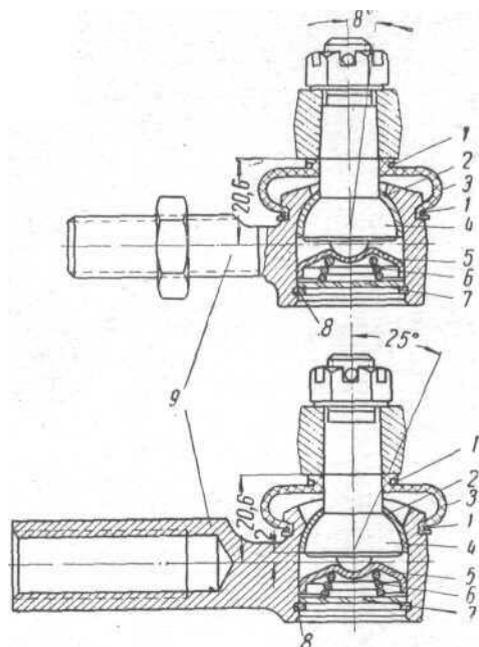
Шарниры рулевых тяг автомобиля модели 407 (вверху правый шарнир правой тяги, внизу шарнир левой тяги): 1 — стяжное кольцо; 2 — опорный вкладыш; 3 — грязезащитный чехол; 4 — шаровой палец; 5 — нажимной вкладыш; 6 — пружина; 7 — заглушка; 8 — стопорное кольцо; 9 — наконечник
